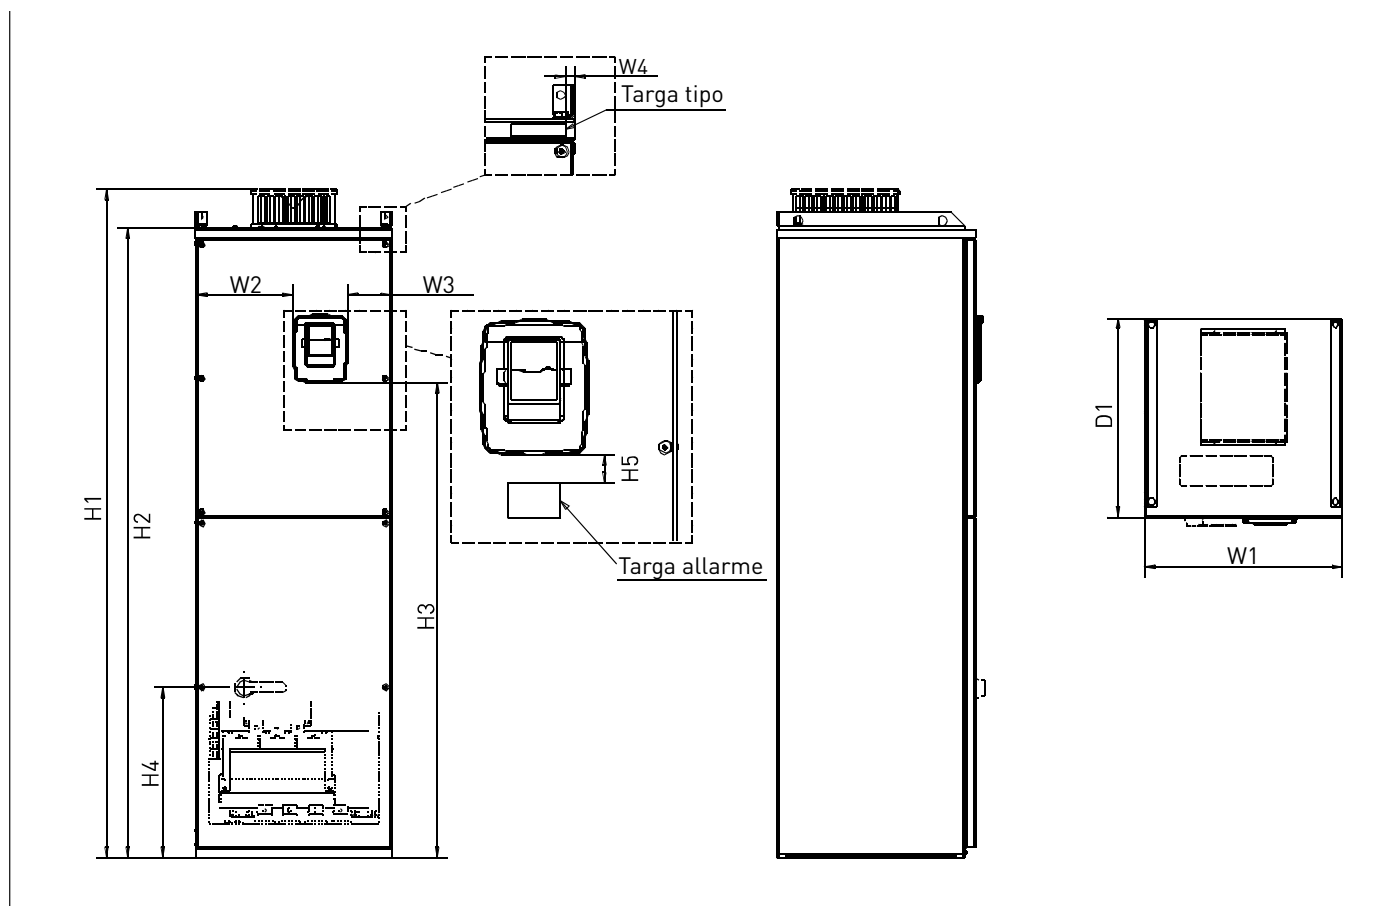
Dimensioni di ingombro dei Vacon NX\_, FR10 e FR 11 (unità a terra)
